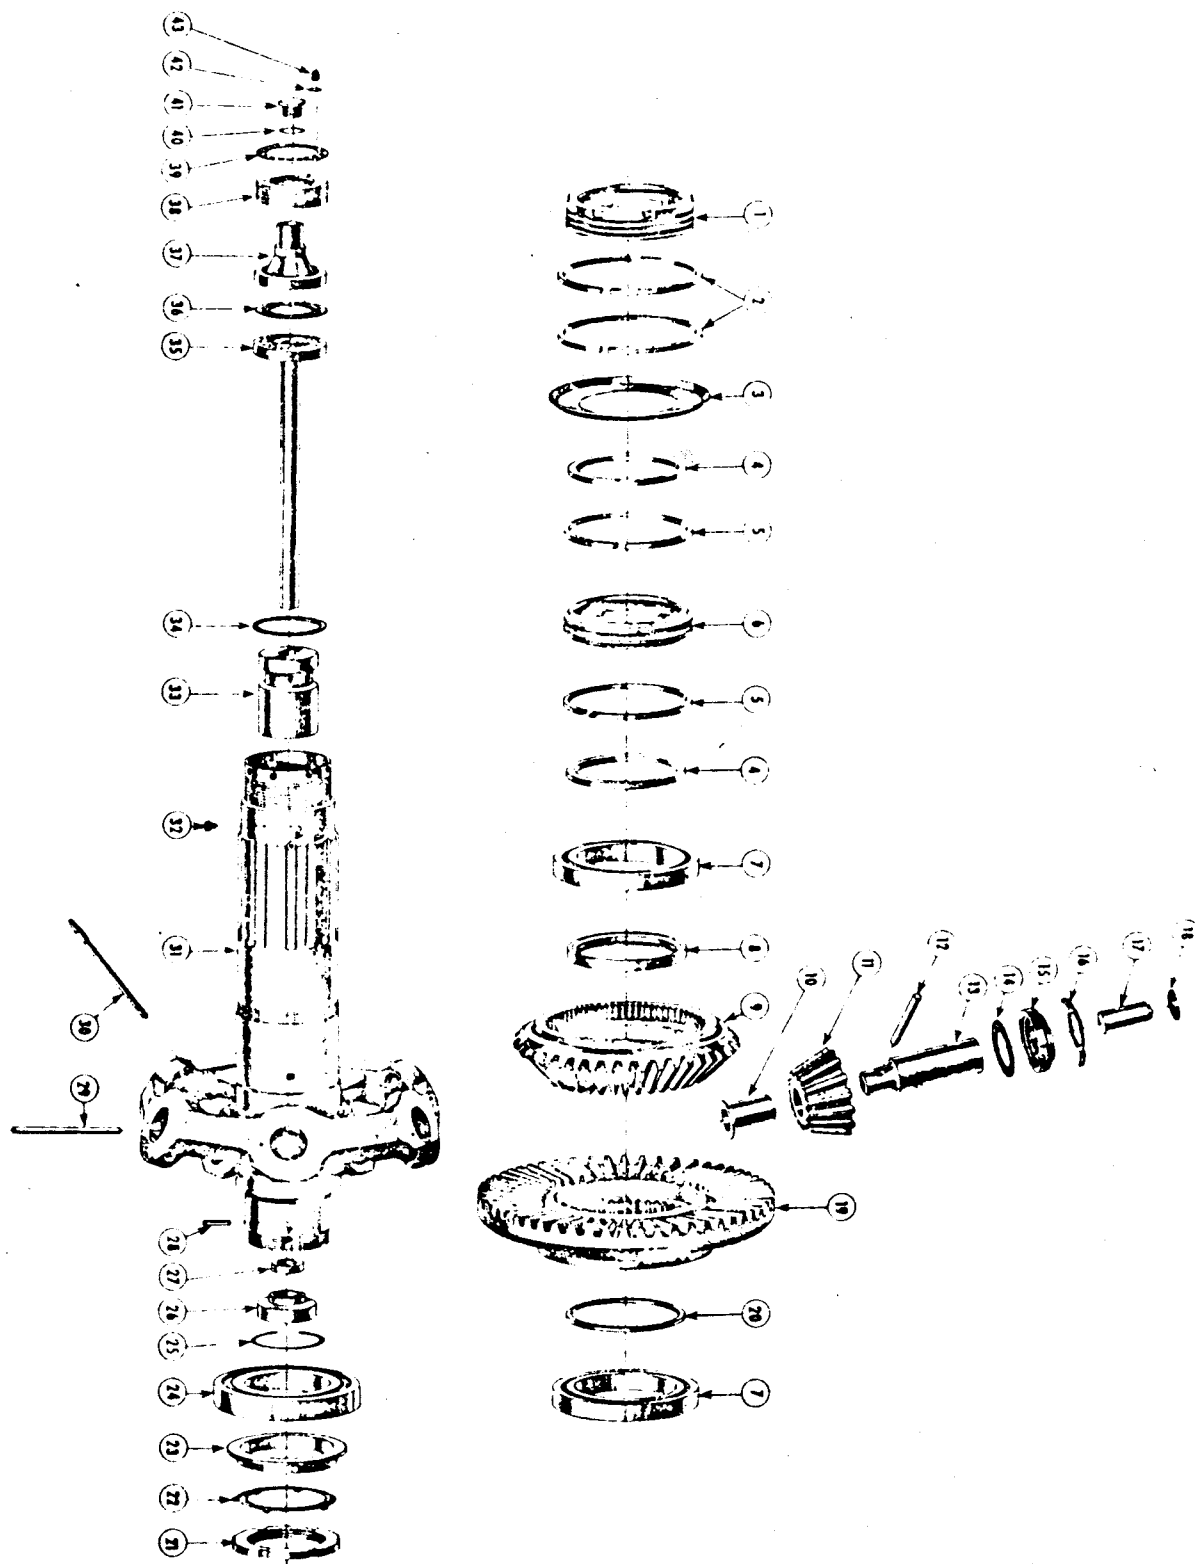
ENGRENAGES RÉDUCTEUR 92
